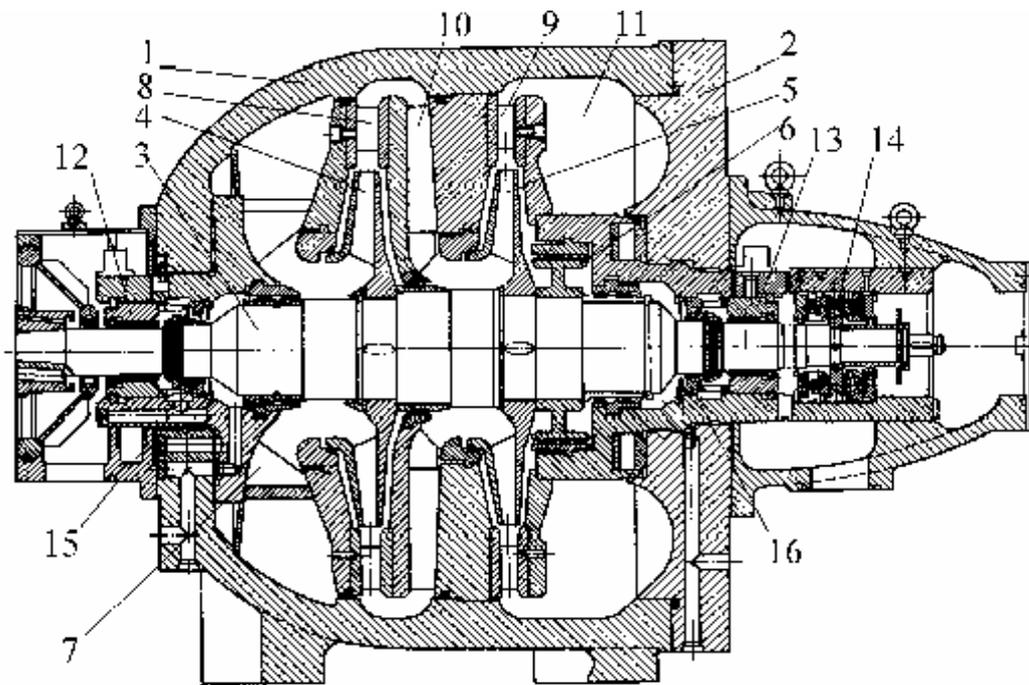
Двухступенчатый центробежный компрессор конструкции НЗЛ
